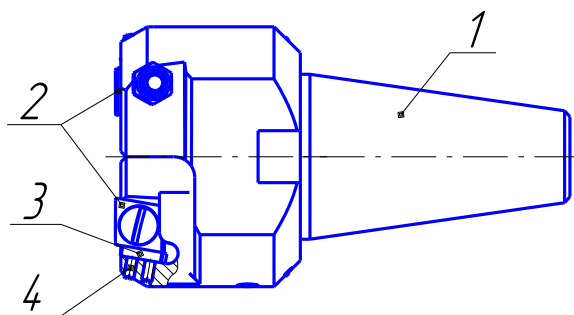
Спеціальна інструментальна головка для остаточної обробки Хрестовини
